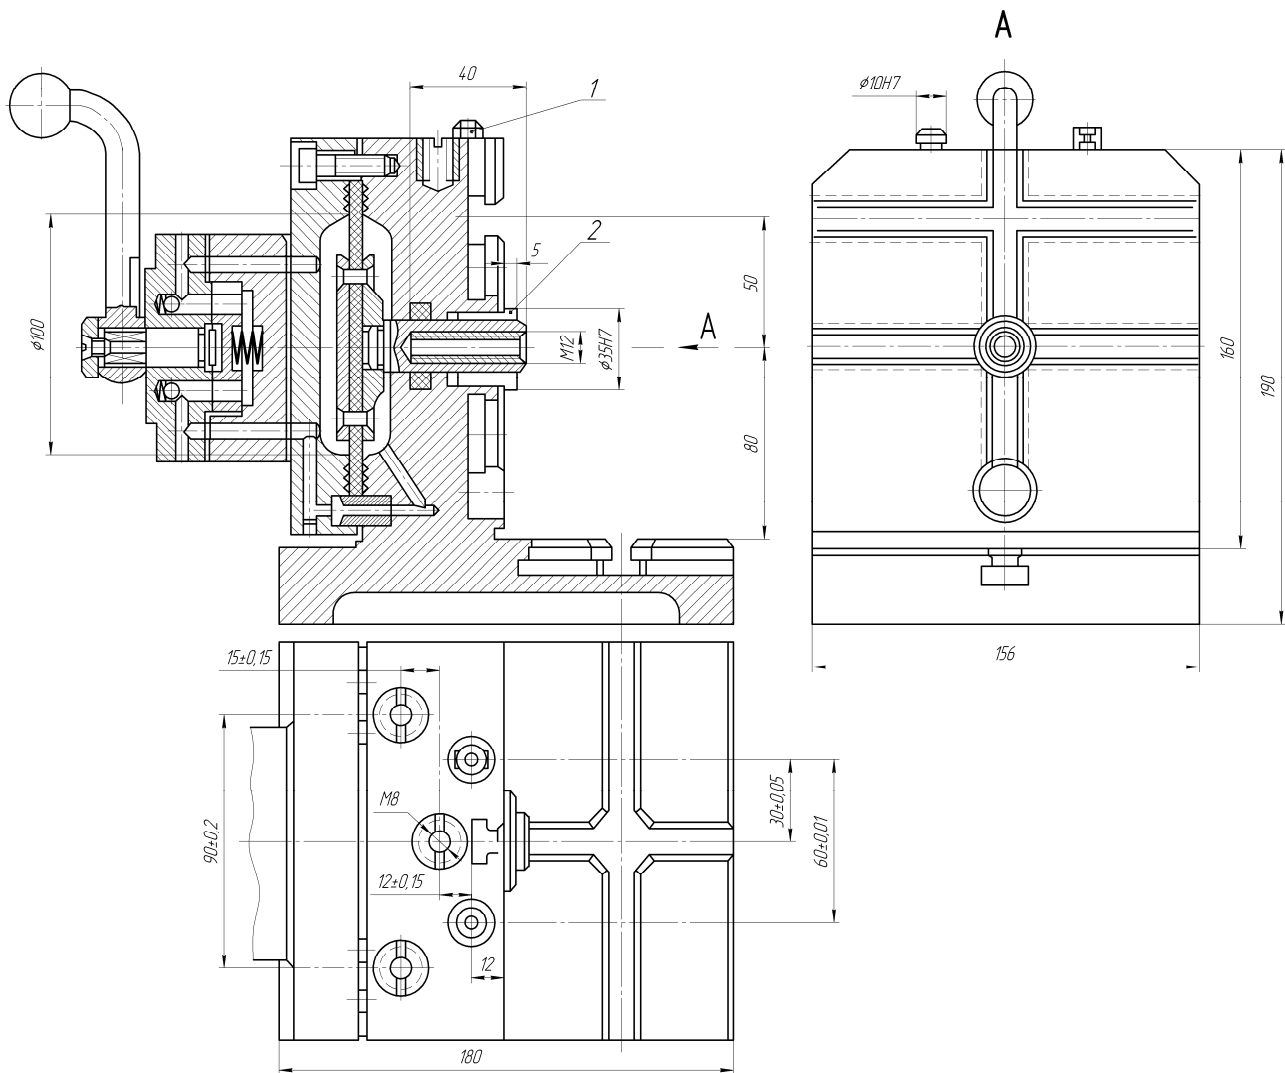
Будова й параметри стола кутового для закріплення заготовок невеликого розміру з подальшим фрезеруванням або свердлінням: 1 – палець; 2 – втулка
